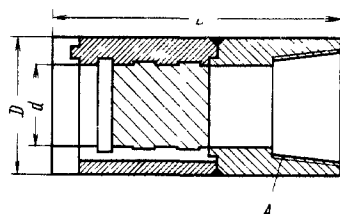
Фрезер режущо-истирающий кольцевой
